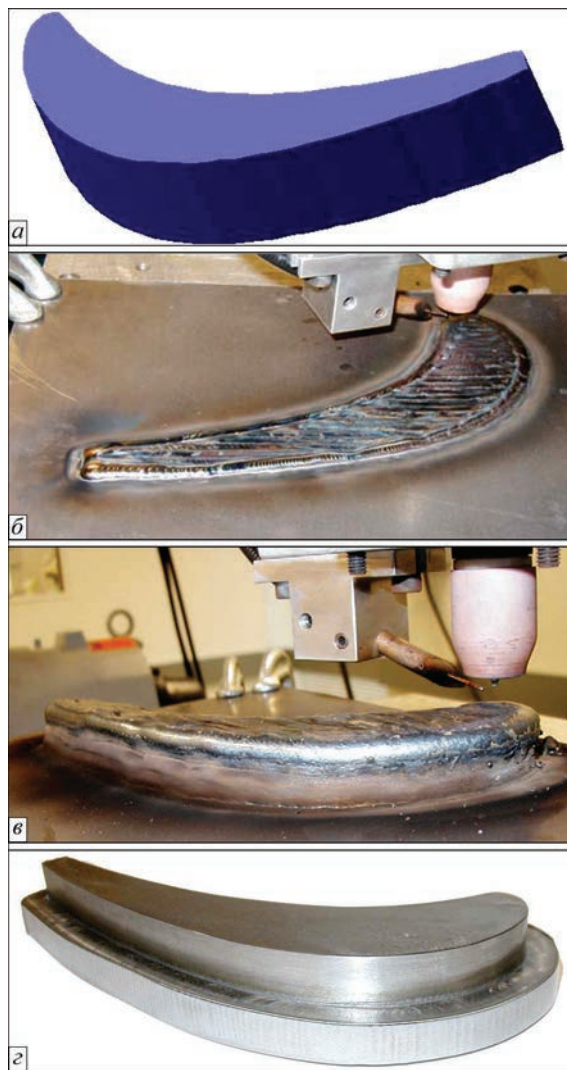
Процесс изготовления лопатки турбины при помощи сочетания дуговой наплавки и ЧПУ-фрезерования: *a* – CAD-модель; *б* – начало TIG-наплавки; *в* – окончание TIG-наплавки; *г* – заготовка после ЧПУ-фрезерования [13]
